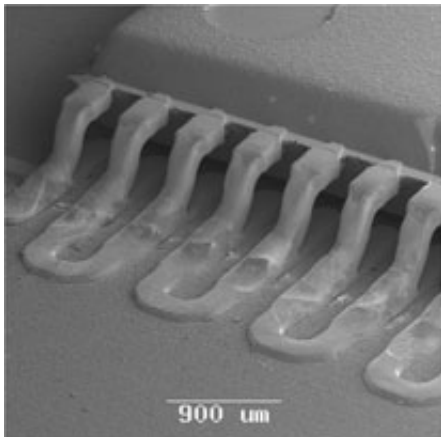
Eine mögliche Anwendung des neuen Scanners ist das Schweißen von Mikroelektronischen Bauteilen. Die abgebildeten Schweißungen wurden jedoch noch nicht mit dem neuen Scanner durchgeführt
